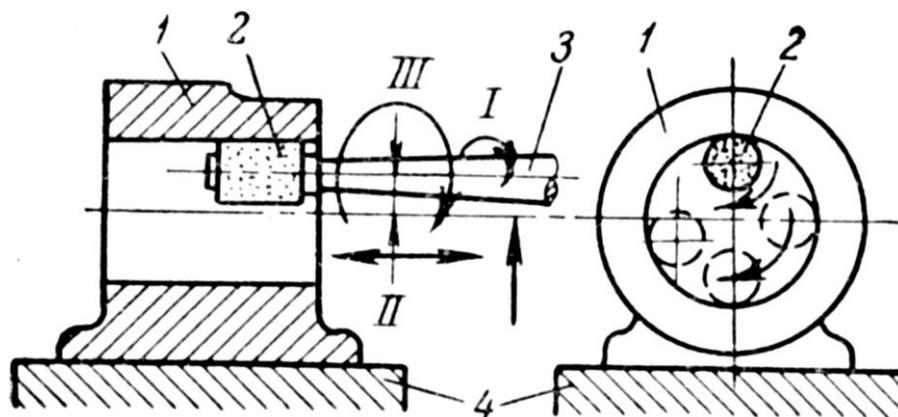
Схема работы внутришлифовального станка с планетарным движением шпинделя
